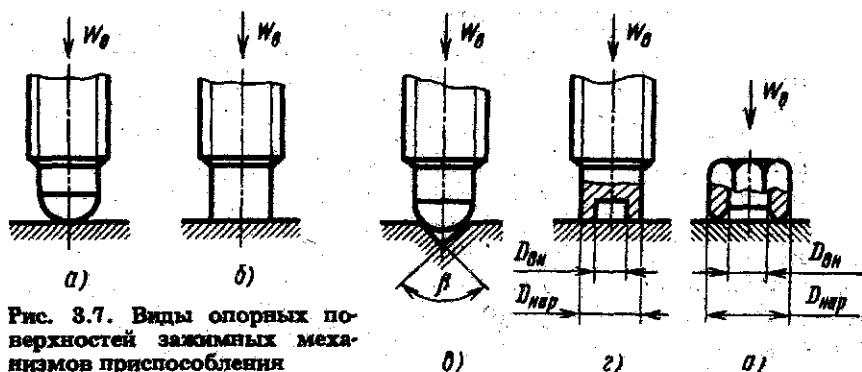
Виды опорных поверхностей зажимных механизмов приспособления
